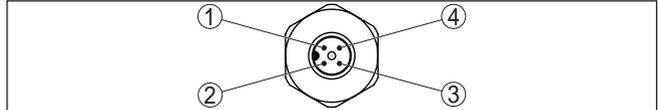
Sicht auf den Steckverbinder (M12 x 1-Stecker - 4-polig)
